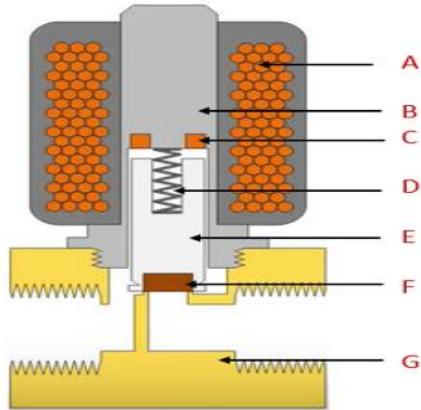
Componentes de una electroválvula; bobina (A); carcasa (B); anillo de sombreado (C); muelle (D); émbolo (E); junta (F); cuerpo de la válvula (G)
